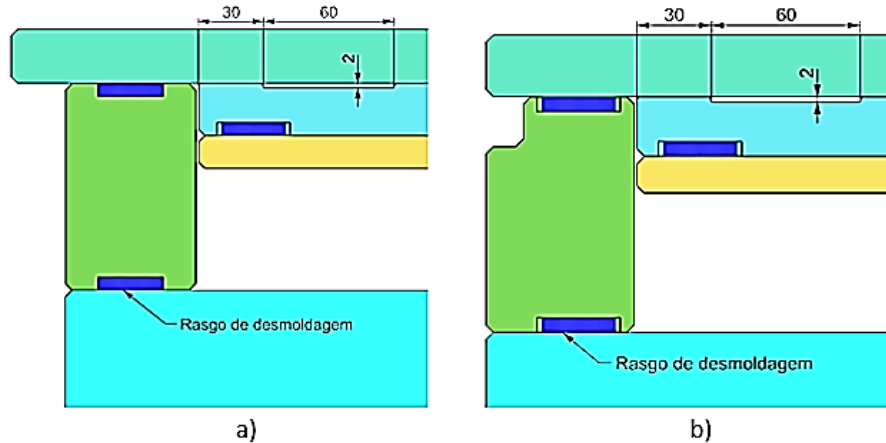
a) e b) construção da estrutura do molde (Grupo Simoldes, 2016)
